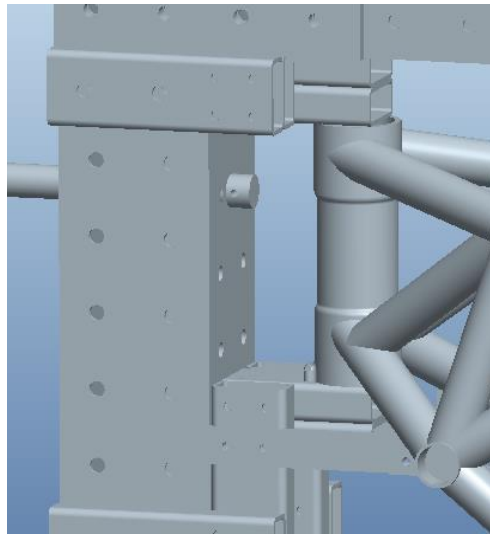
Conjunto auxiliar del potro de soldadura formado por conjunto de tubos
